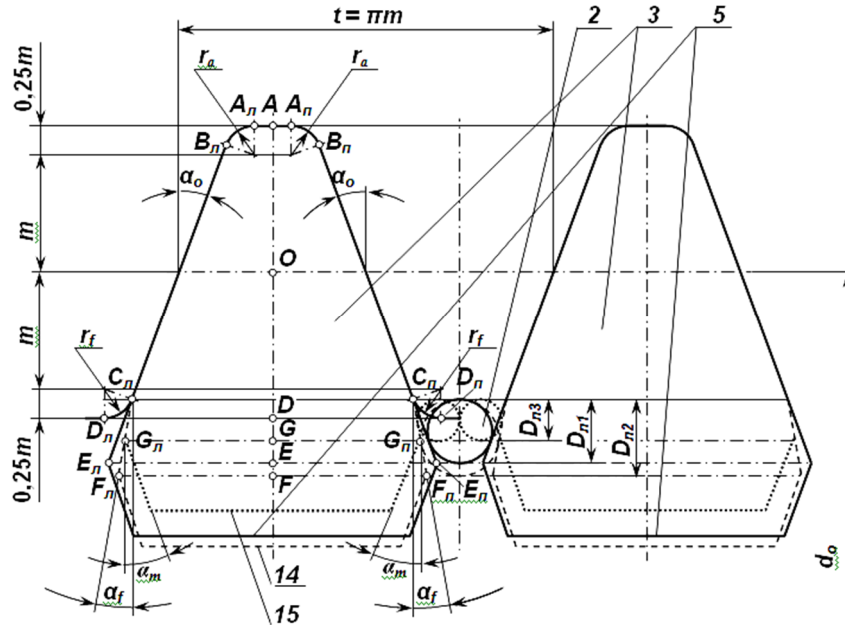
Параметры профиля быстросменных режущих пластин для червячного шевера и пружин, введенных между их ножками
